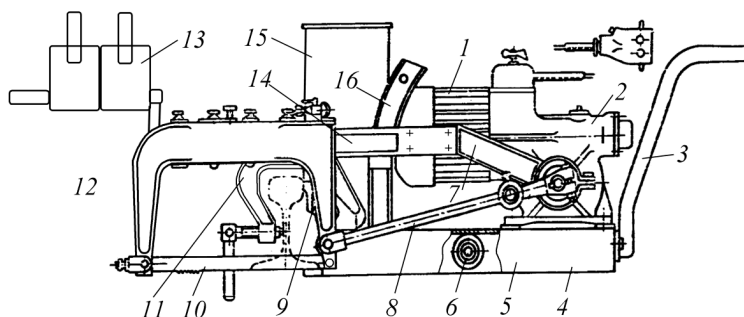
Рейкорізальний верстат РМ-2:
